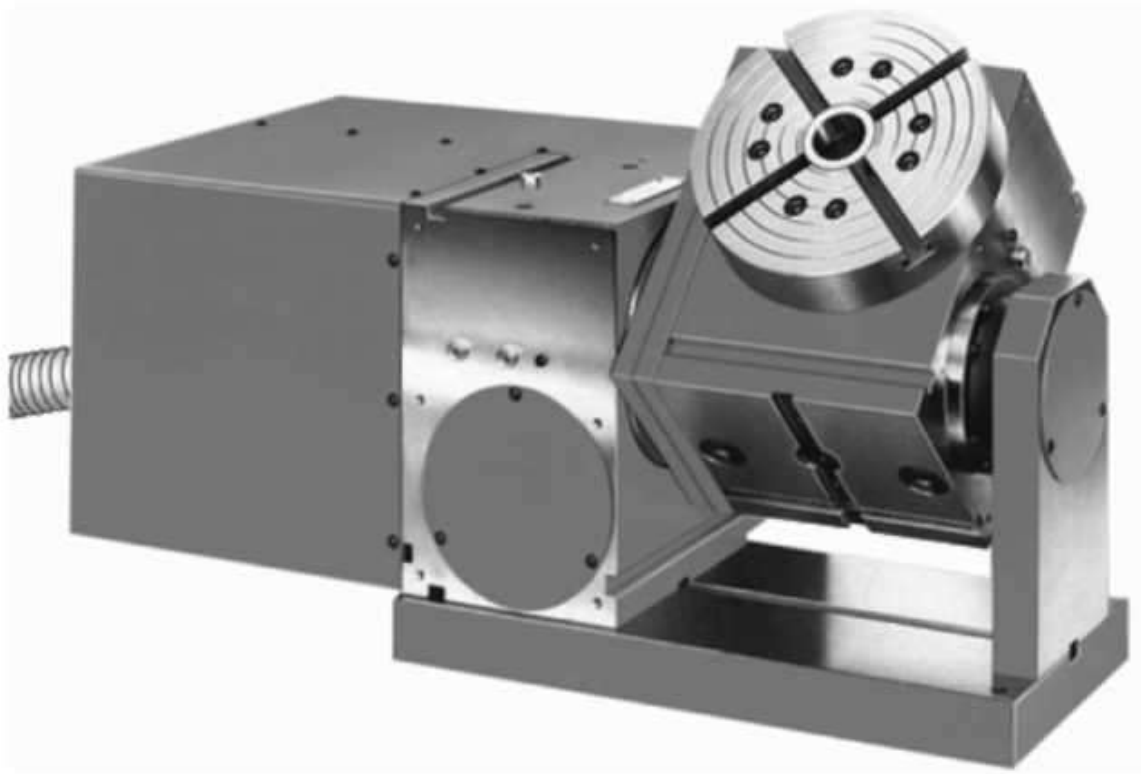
Універсальний пристрій для обробки поверхонь заготовок різних діаметрів під різними кутами
